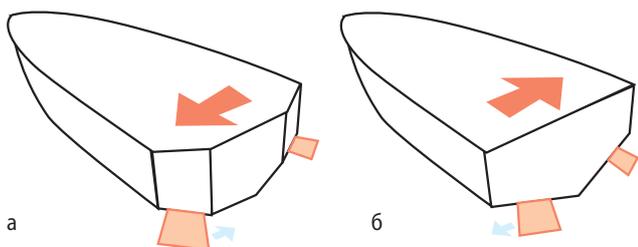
Перед установкой плит на скругленный в плане транец придется снабдить его накладными переходниками
